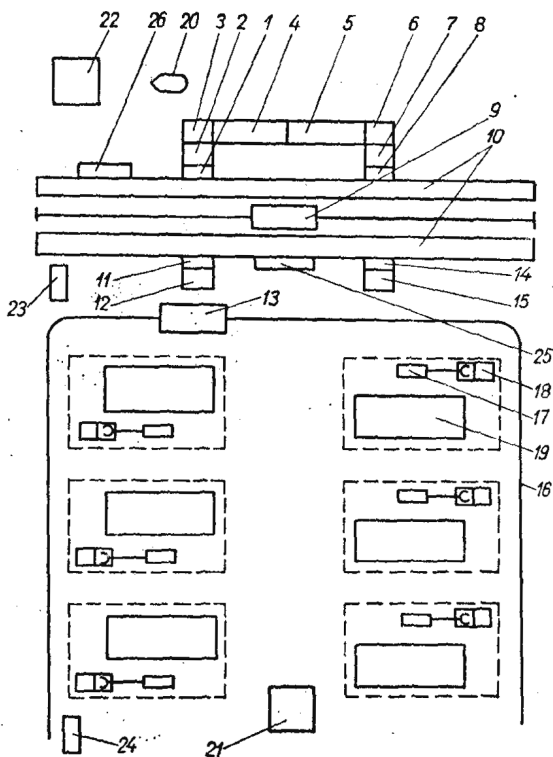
Компонівка гнучкої автоматизованої ділянки обробки деталей типу «тіла обертання» на ВО «Конвейер».
